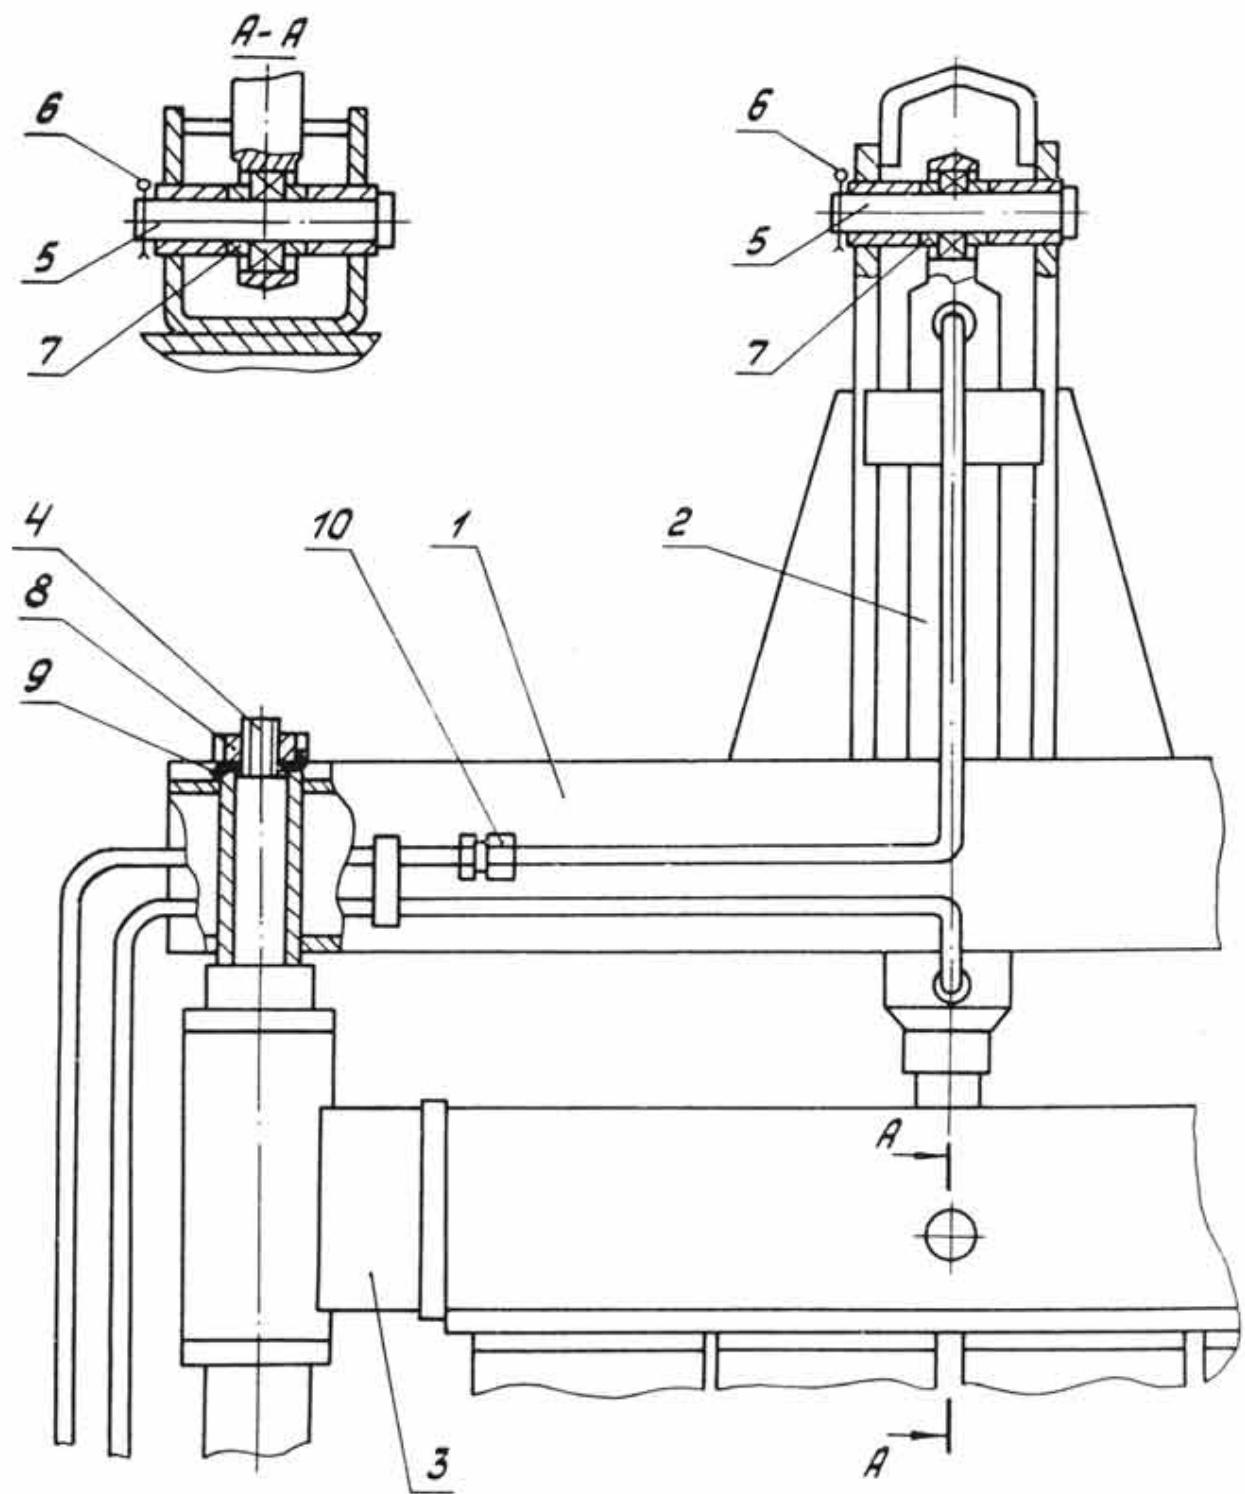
Узлы крепления балки и гидроцилиндра пресса
